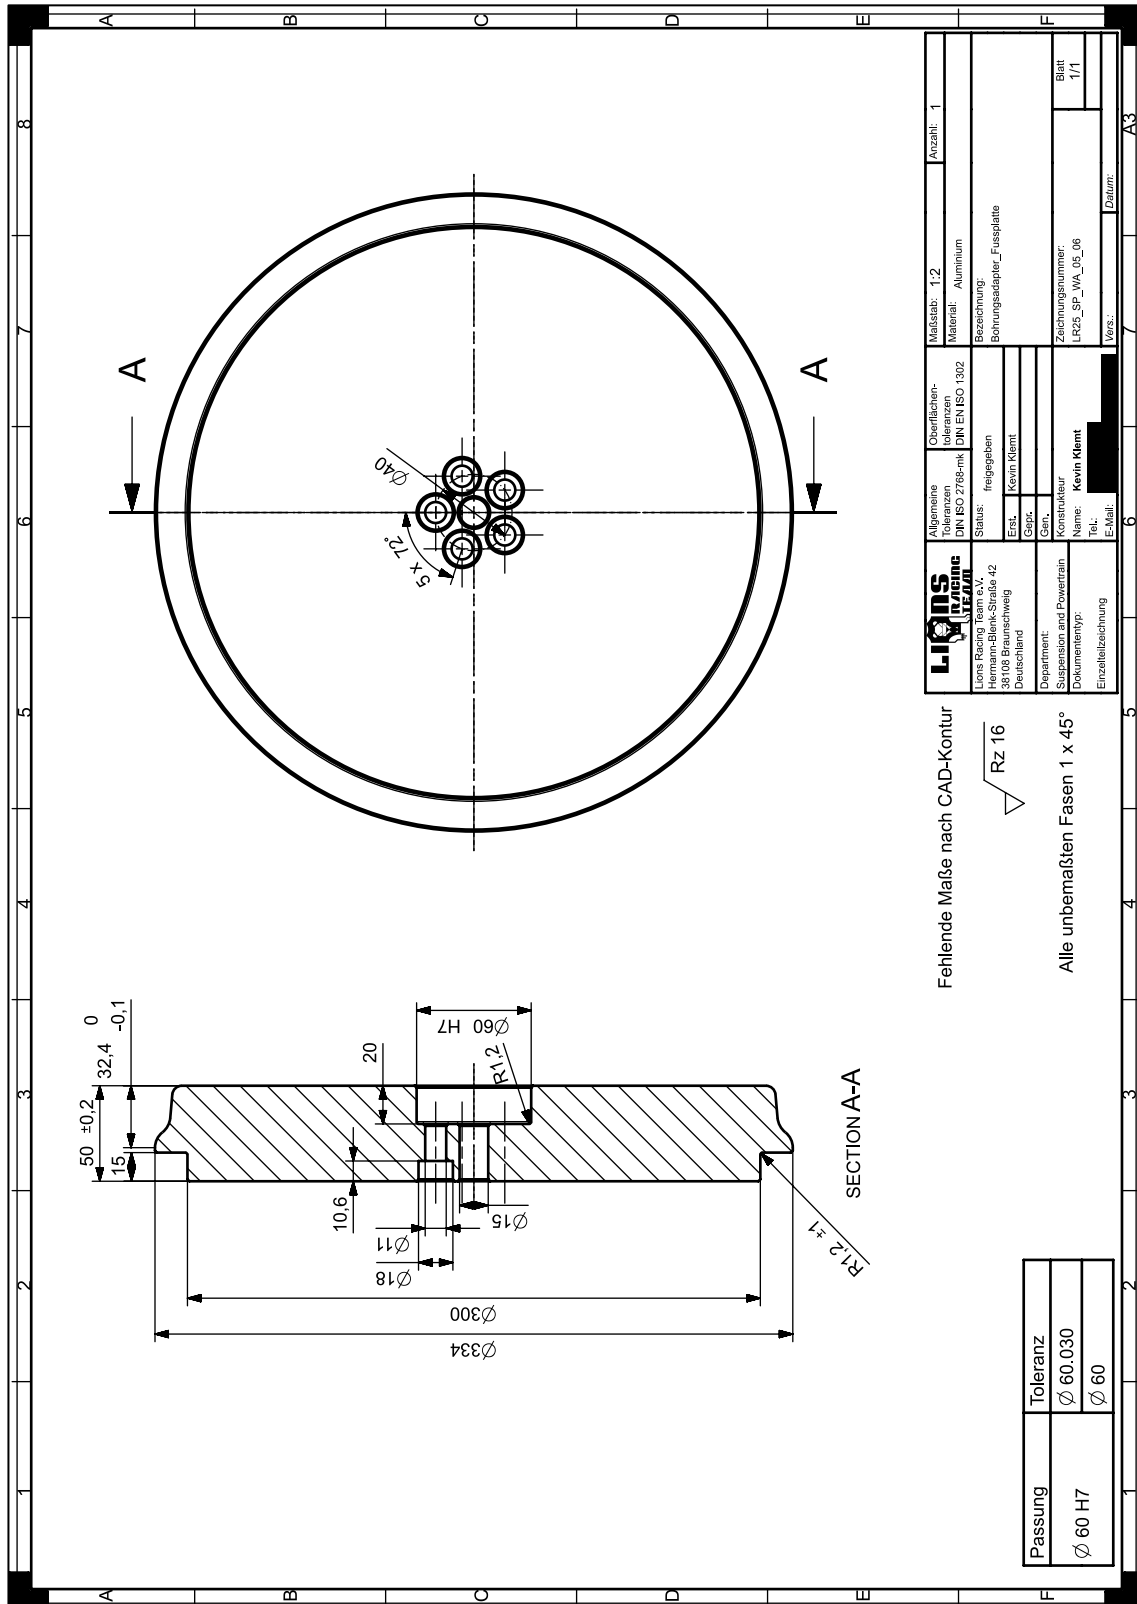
Technische Zeichnung Bohradapter (2/4); Fußplatte [42]
